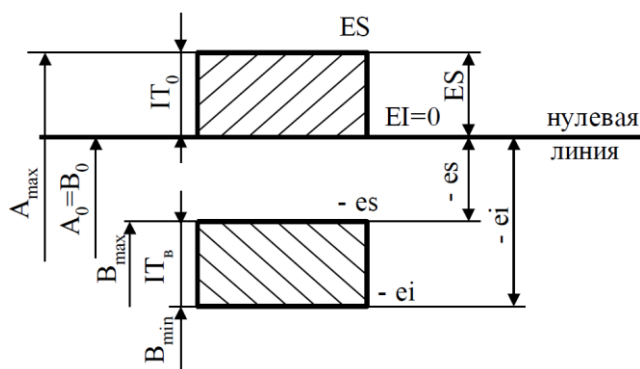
Схема изображения полей допусков отверстия и вала
